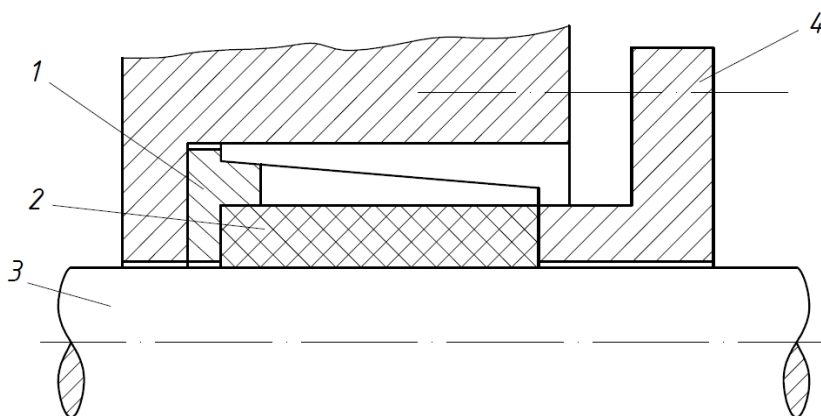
Конструктивная схема сальникового уплотнения с гибкой втулкой с продольными прорезями, охватывающей набивку
